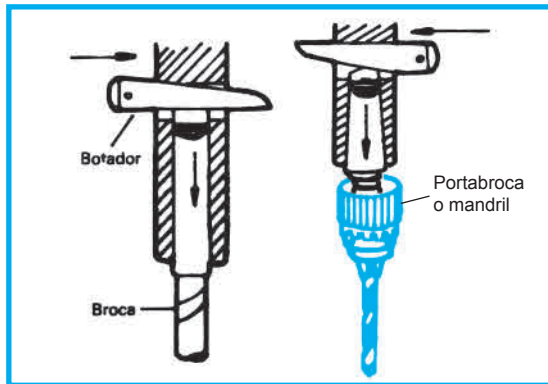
Uso del botador para extraer brocas y el mandril.
